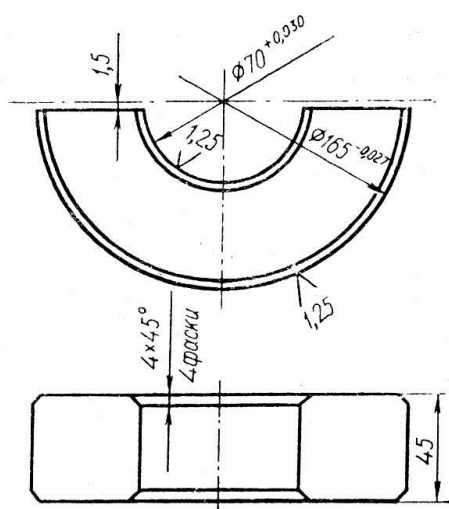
Установочні вкладиші для різцевої борштанги.
